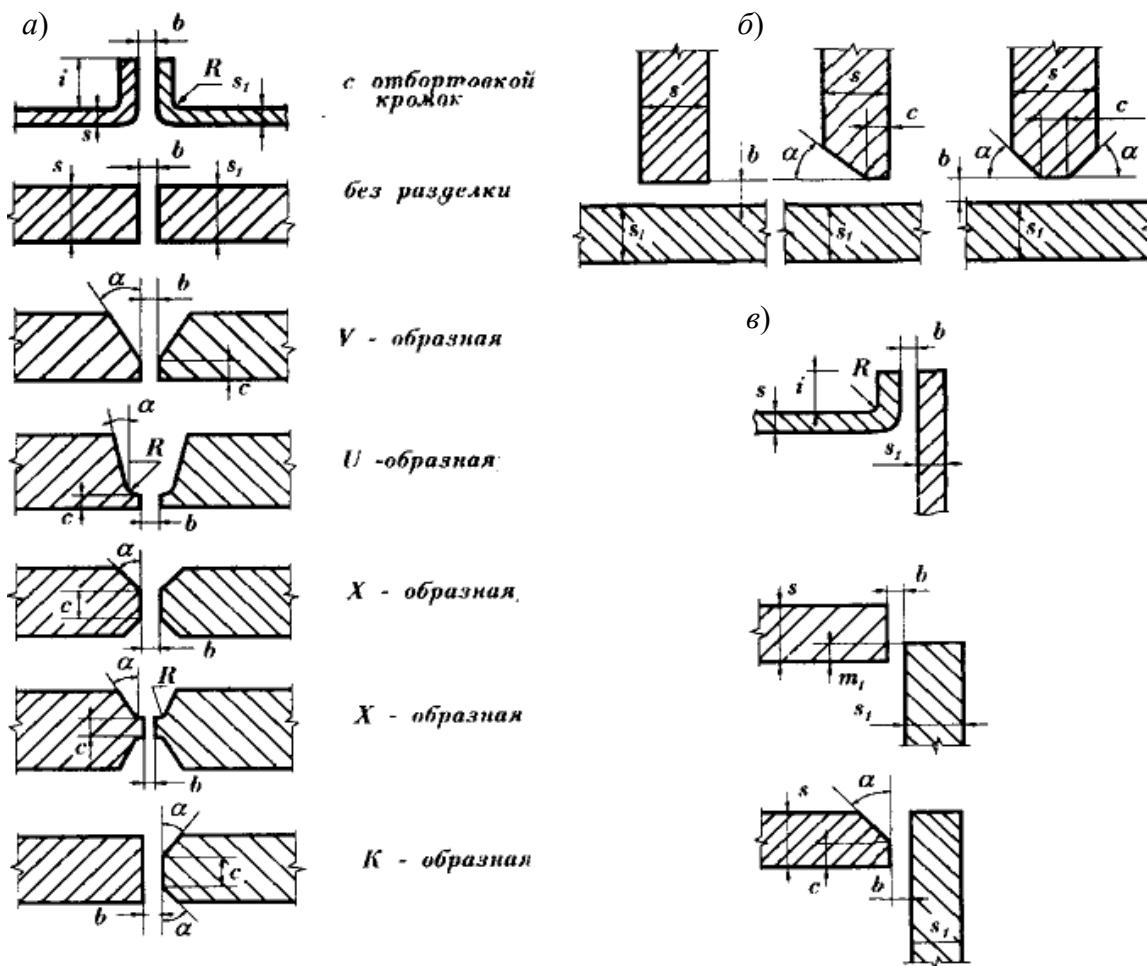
Форма подготовки кромок свариваемых элементов
